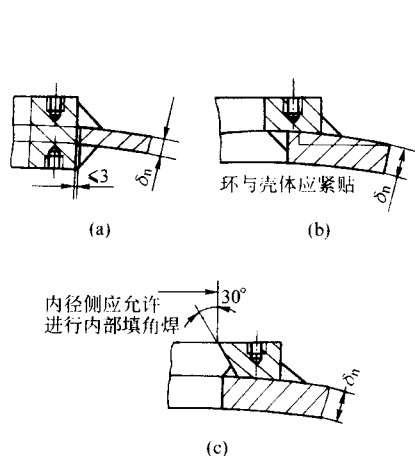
凸缘与壳体连接的非焊透接头形式
